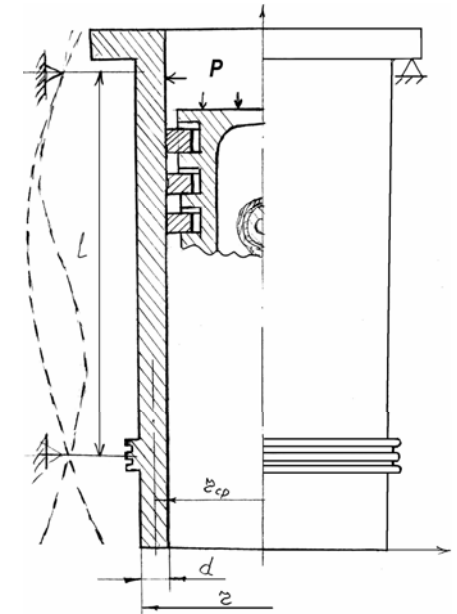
Типовая схема цилиндрической втулки тронкового двигателя
